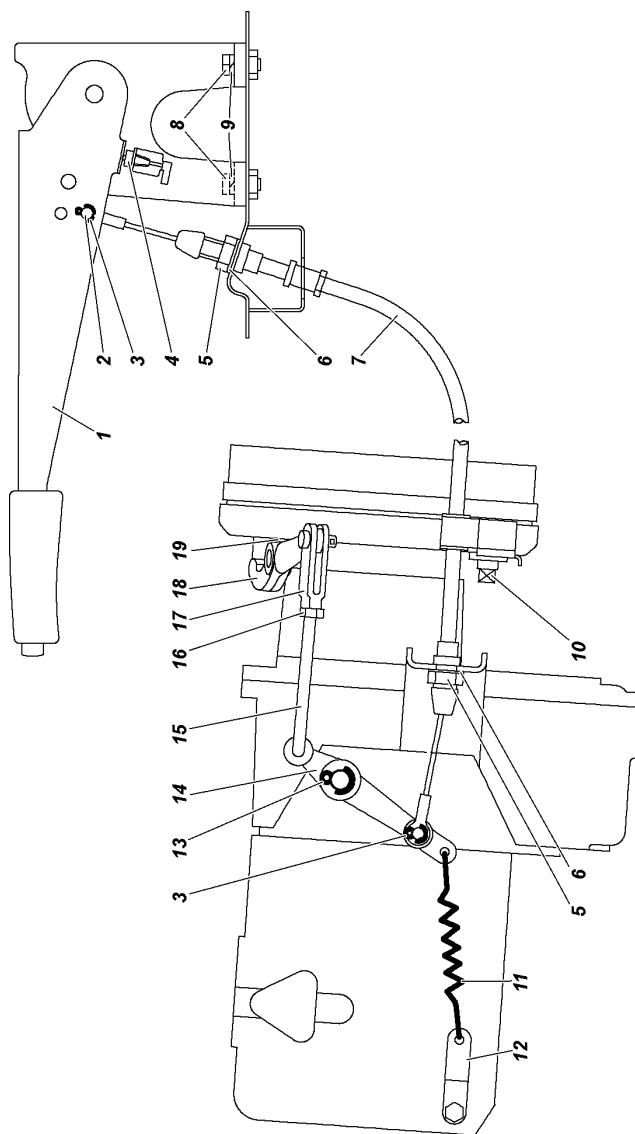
Привод стояночного тормозного механизма для автомобилей с четырехступенчатой коробкой передач:
